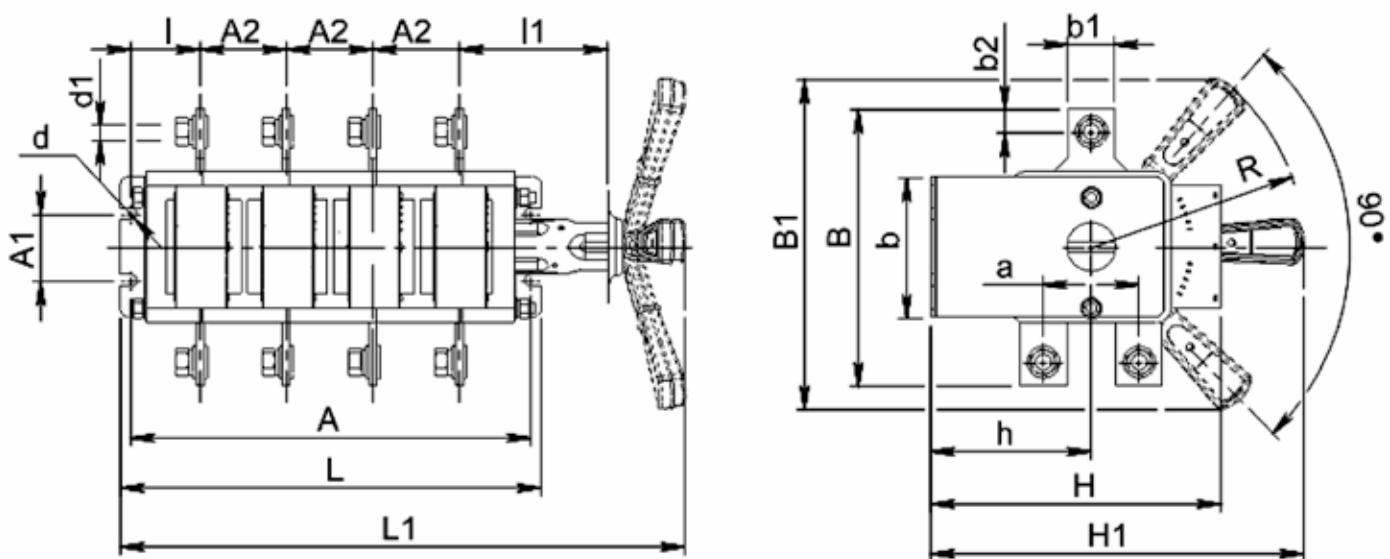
Выключатель-разъединитель на два направления 4-полюсный с боковой смещенной рукояткой
